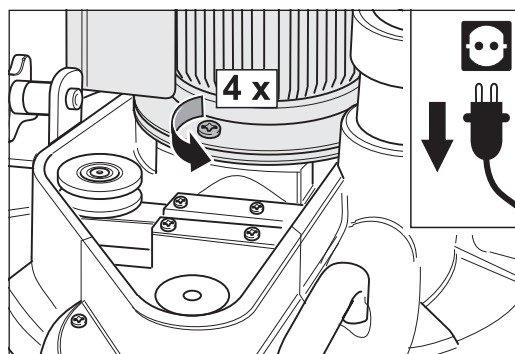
Die vier Befestigungsschrauben des Motors entfernen.
